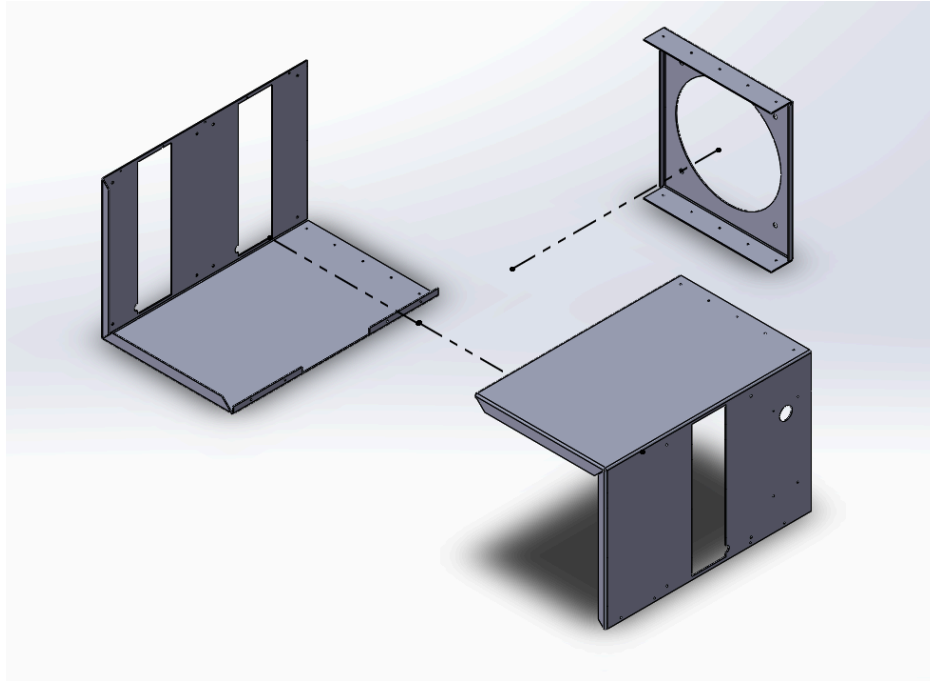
Vista explosionada de las partes que forman el cuerpo del prototipo
